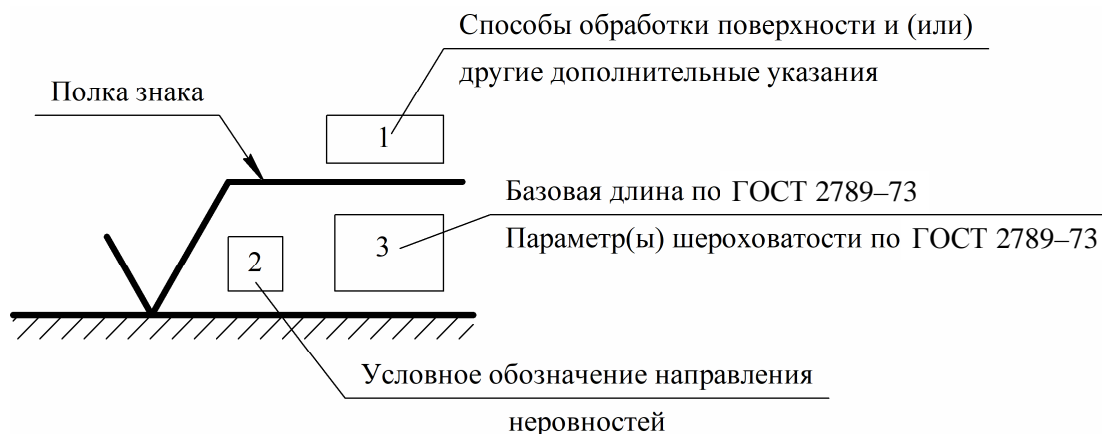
Структура обозначения шероховатости поверхностей
